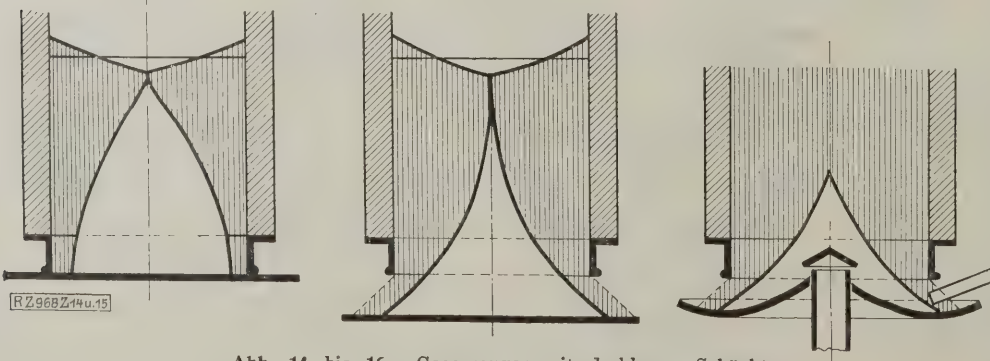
bis 16. Gaserzeuger mit drehbaren Schächten.
